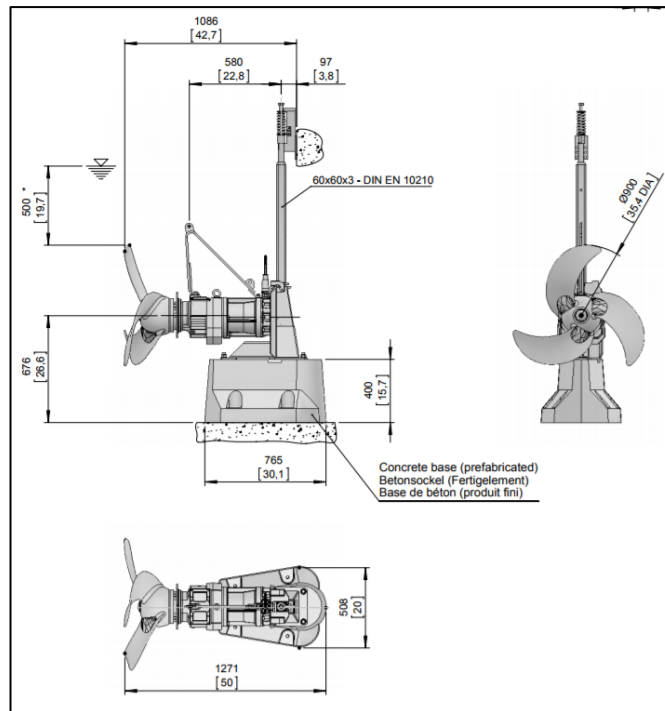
Alzado, planta y perfil de agitador de 900 mm de diámetro
